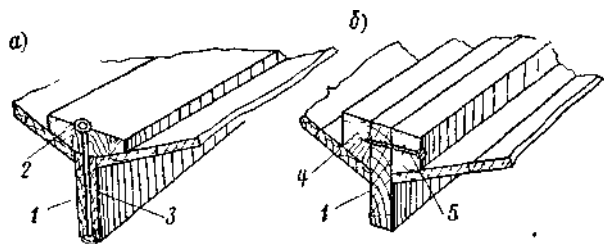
Два способа сборки килей: а — с резен-килем из доски; б — с боковыми рейками.
